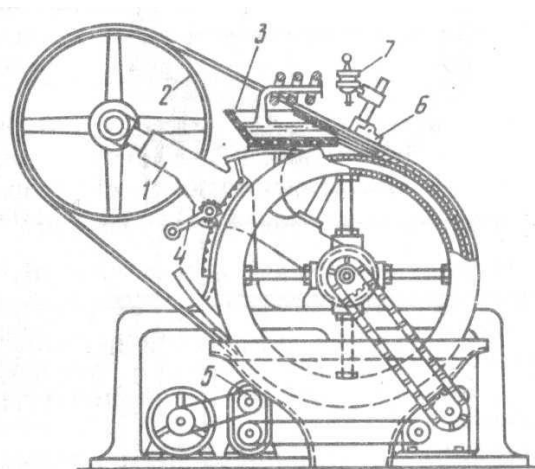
Схема машины с роторным кристаллизатором (установка Проперцы): 1 – качающийся рычаг; 2 – направляющий ролик ленты; 3 – разливочное устройство; 4 – рукоятка; 5 – регулятор скорости; 6 – пористый лист; 7 – масленка
